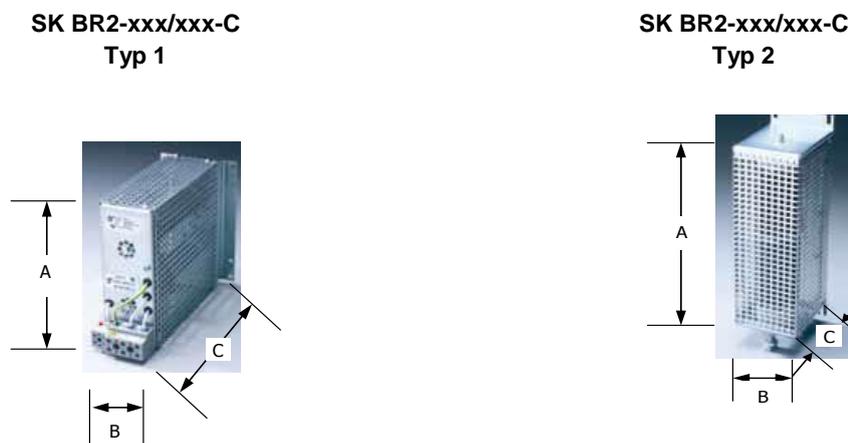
Bemaßungen der Chassis- BW SK BR2/xxx/xxx-C
